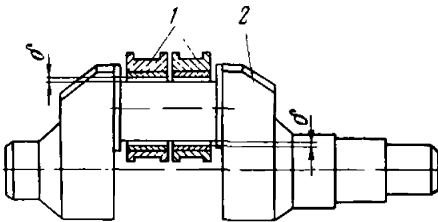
Коленчатый вал с нижней головкой шатуна:
